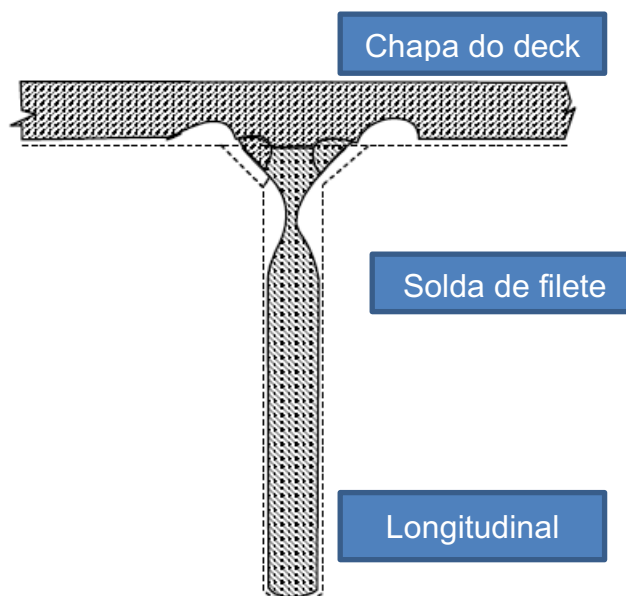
Corrosão de fresta em junta soldada de reforço: chapa do deck (Deck plating); solda de filete (Fillet weld); longitudinal. Fonte: DNV (2013)
